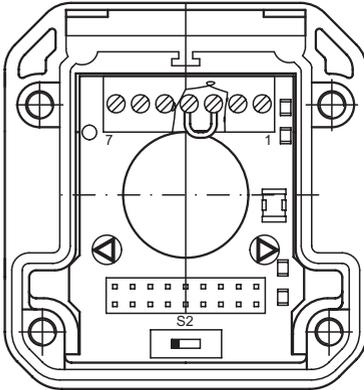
Caperuza del conexión del emisor/T1 desmontada, vista interior del panel de bornes
